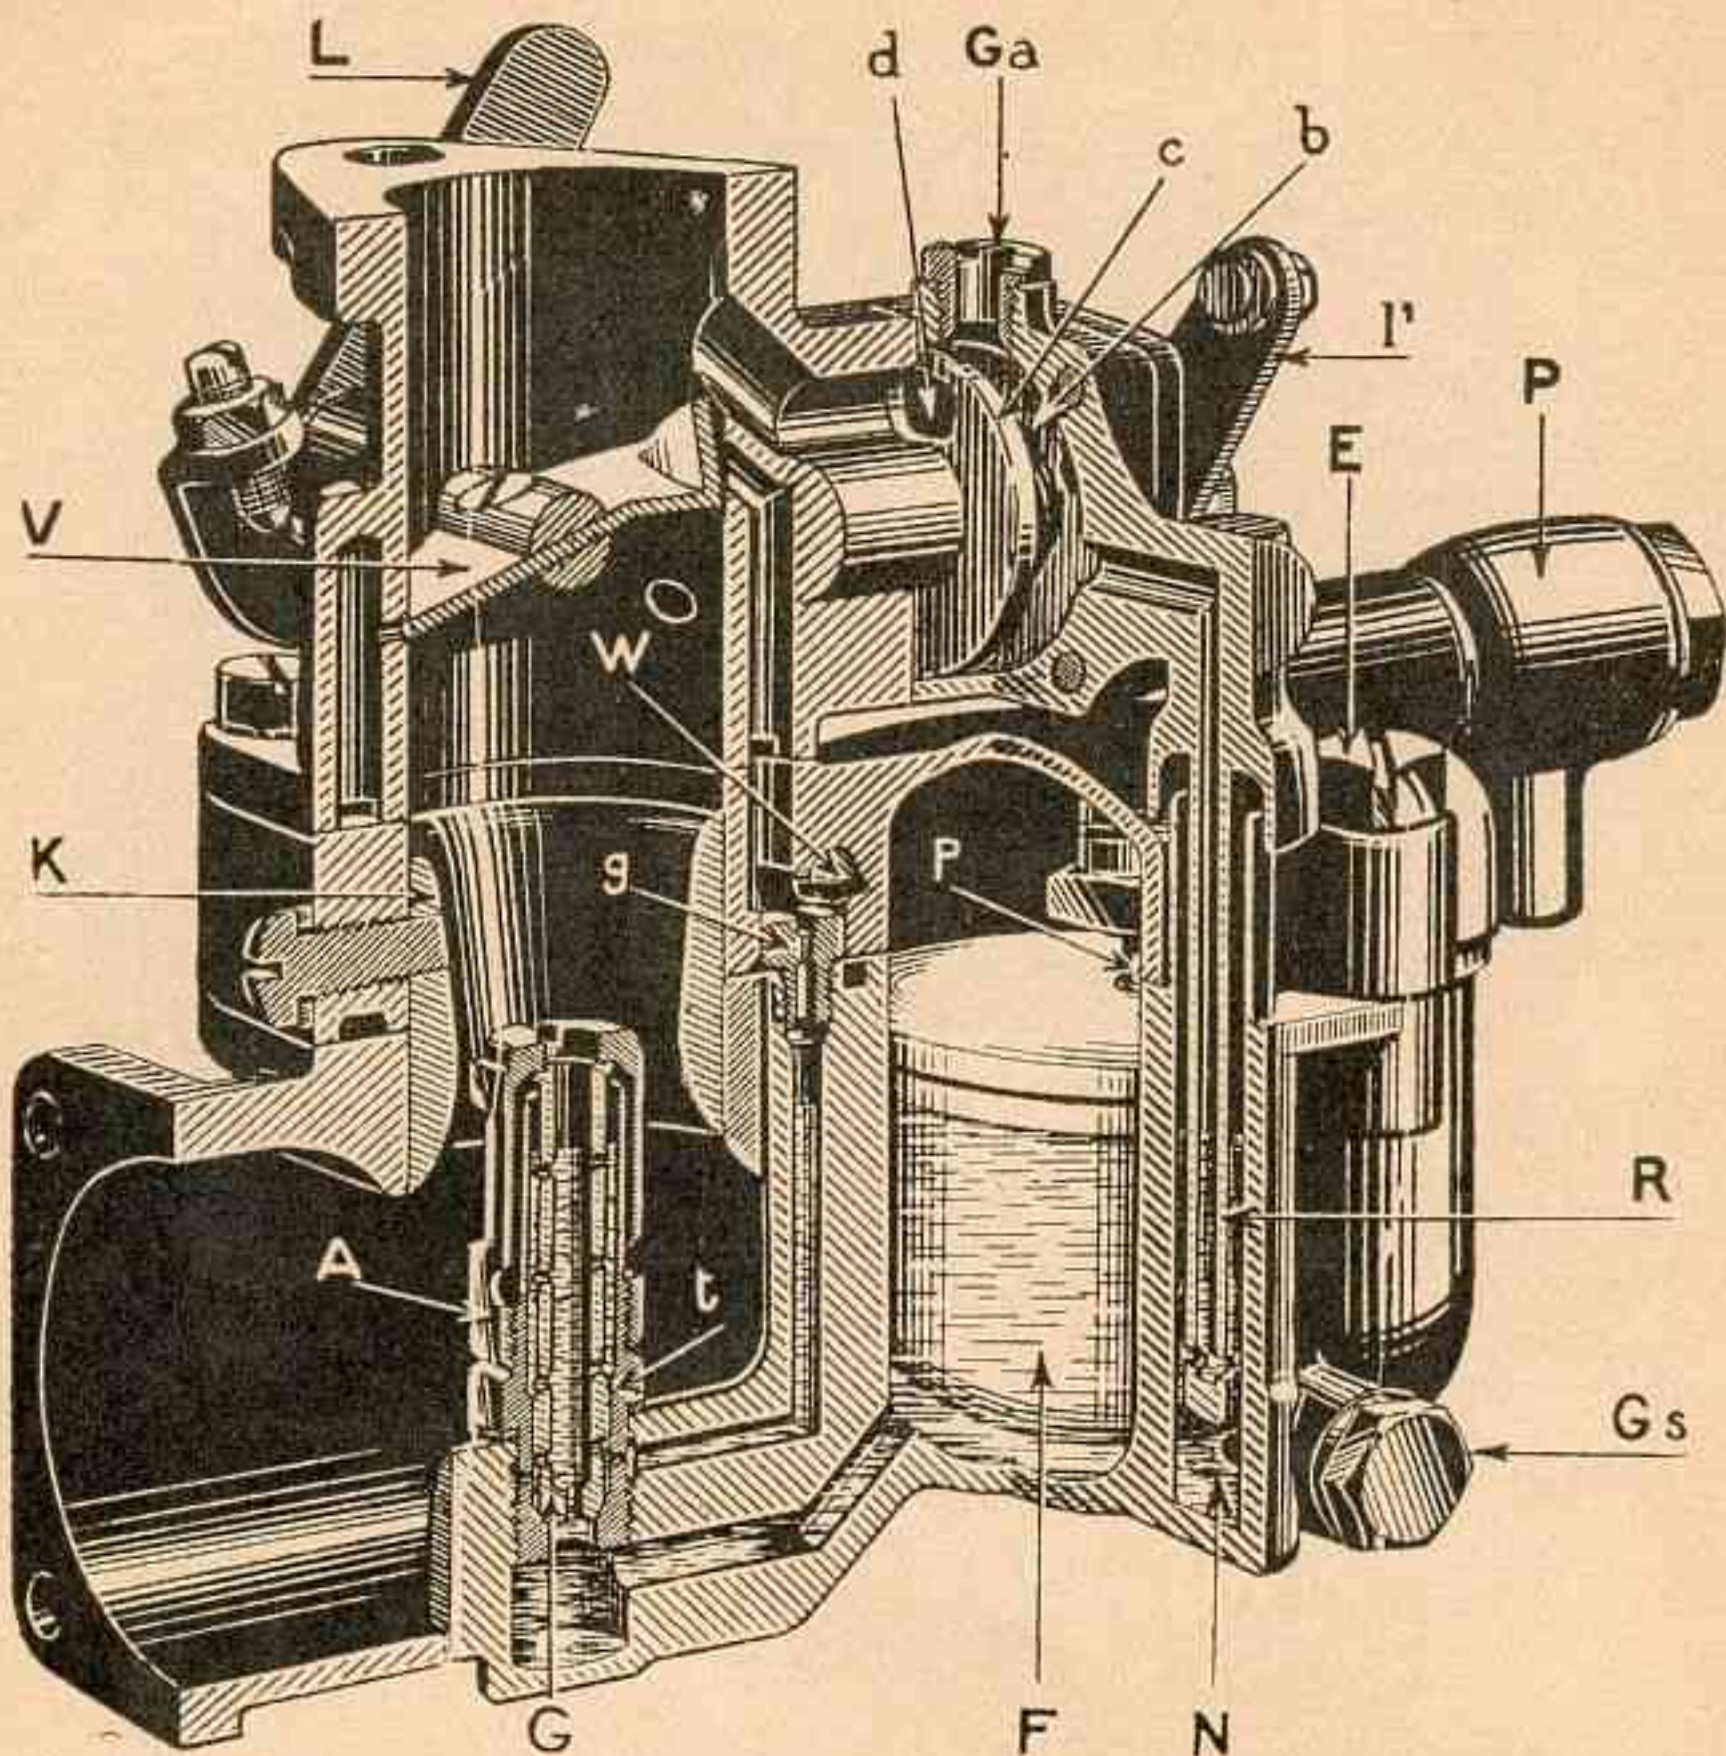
Coupe d'un carburateur vertical SOLEX à starter.
